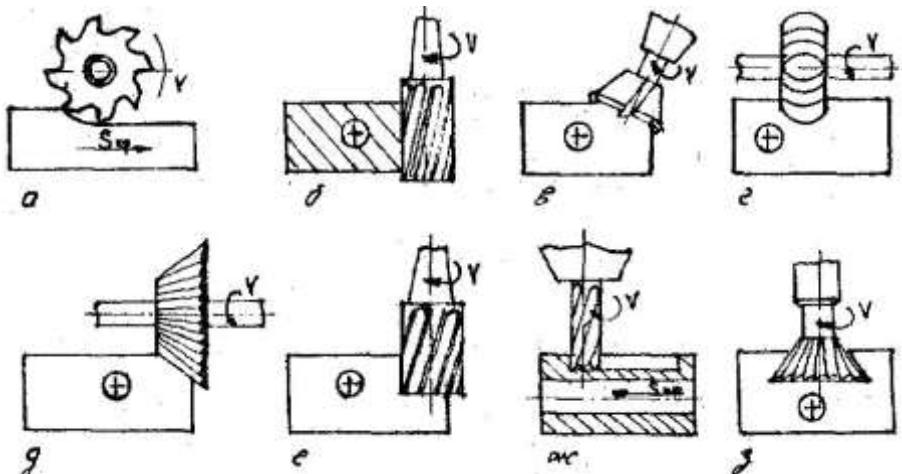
Схеми обробки заготовок на фрезерувальних верстатах
